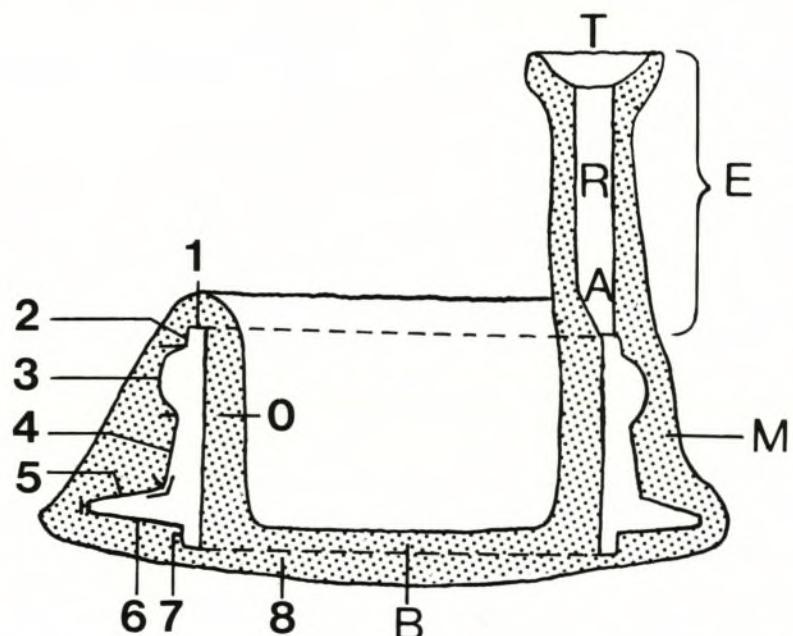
Auerberg. Querschnitt einer Gießform mit Bezeichnung der Formteile. E Einguß; T Trichter; R Röhre; A Anschnitt, M Mantel; B Boden; o-8: die einzelnen Formteile (vgl. Liste 2).
